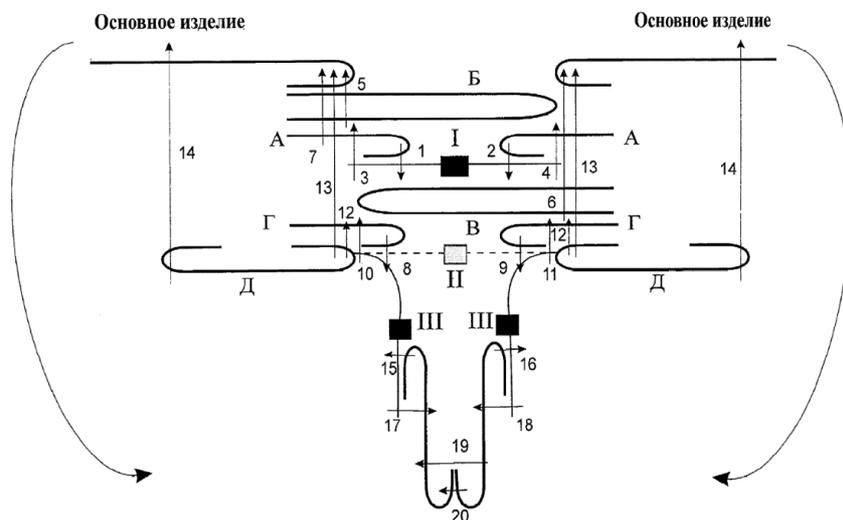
Второй способ обработки специального «кармана» со съемной подкладкой кармана в поперечном сечении из патента RU 2 412 624 С1
